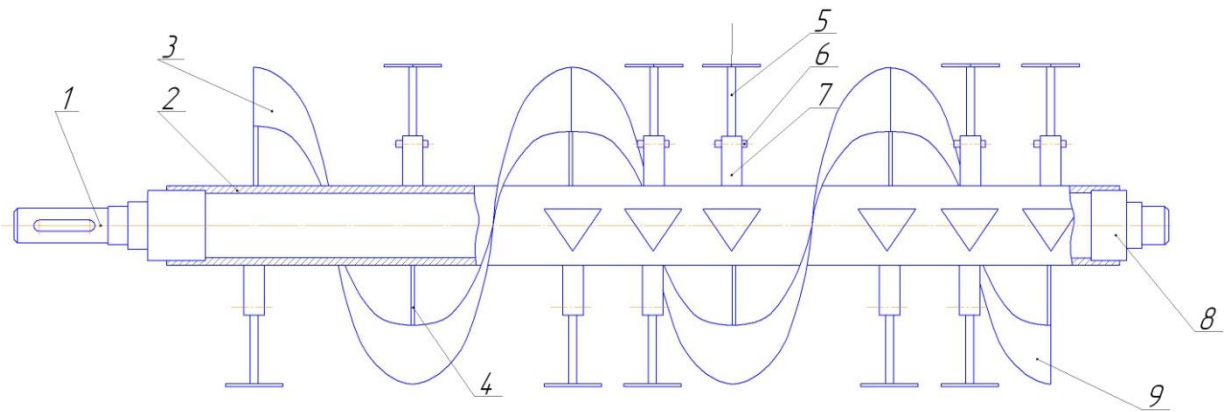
Схема шнекофрезерного рабочего органа погрузчика-смесителя тепличного грунта. 1,8 – опора вала; 2 – вал; 3 – ленточный шнек; 4 – кронштейн ленточного шнека; 5 – стойка с закрепленным зубом; 6 – крепеж; 7 – кронштейн стойки зуба; 9 – секция ленточного шнека
